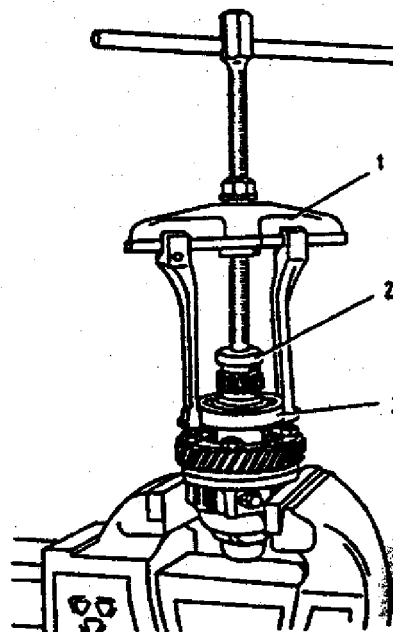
Remoção dos rolamentos: 1 - extrator universal; 2 - apoio 67.7853-9559; 3 - rolamento.
